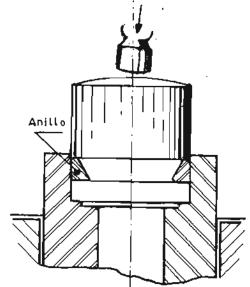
En la morsa con ayuda del cilindro torneado, forzando el anillo externo (montaje en caja).
